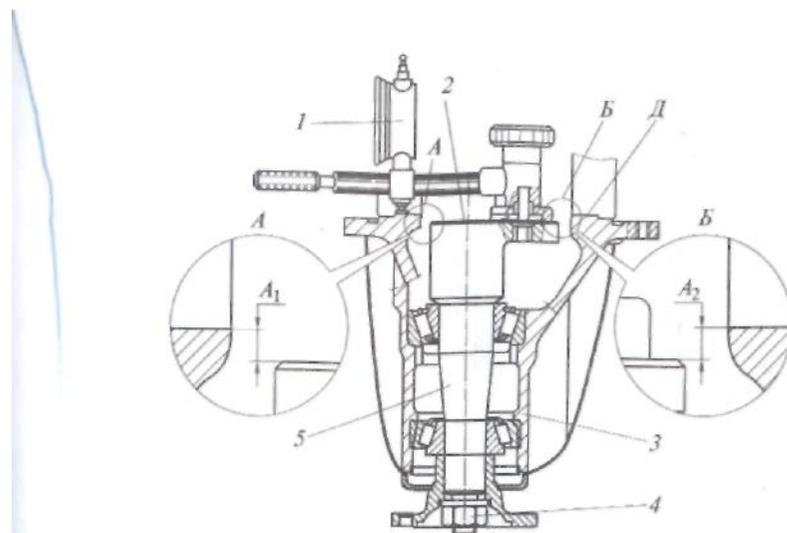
Схема определения толщины регулировочной прокладки (кольца) ведущего колеса:
